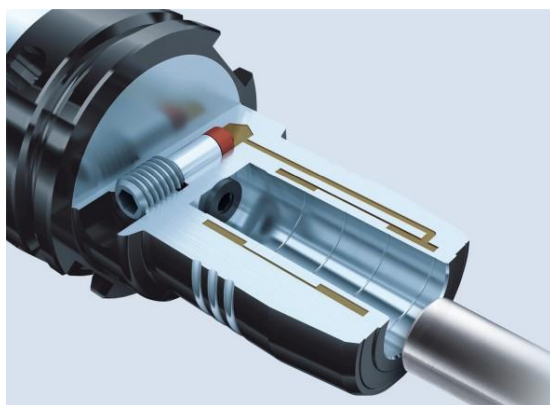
Nástrojová hlava pro frézy s válcovou stopkou [27]
